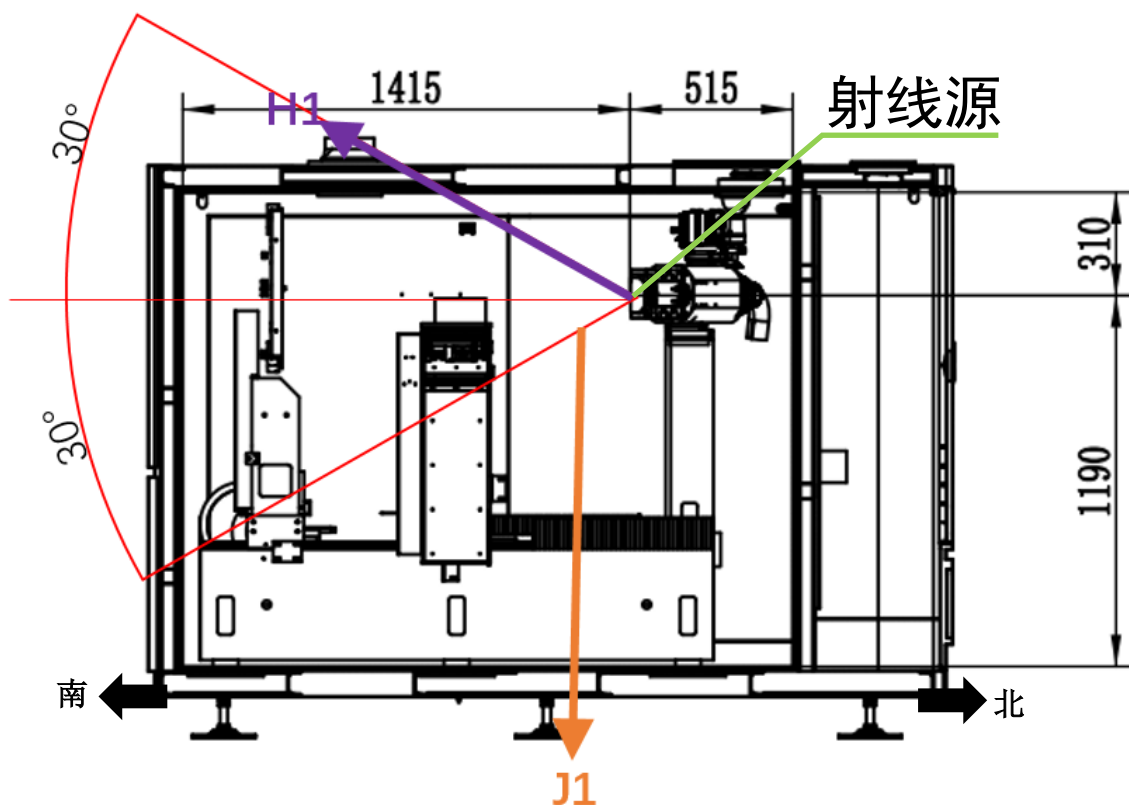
FXO-CT2000 型工业 CT 辐射屏蔽计算预测点位剖面图 (单位: mm)
